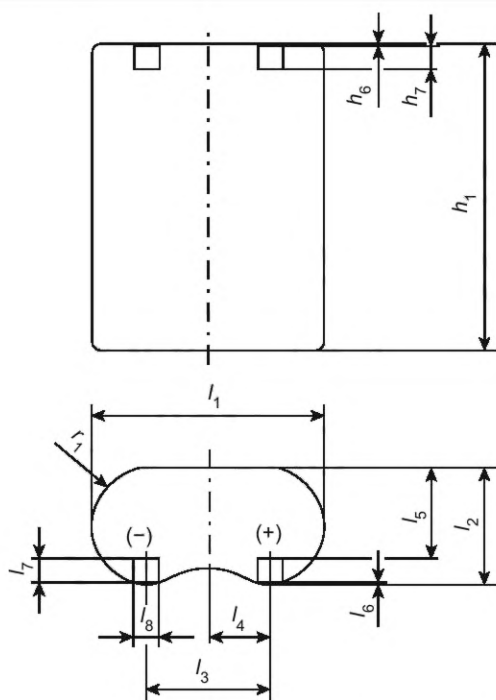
Габаритный чертеж 2CR5 (Cor 1:2022)
